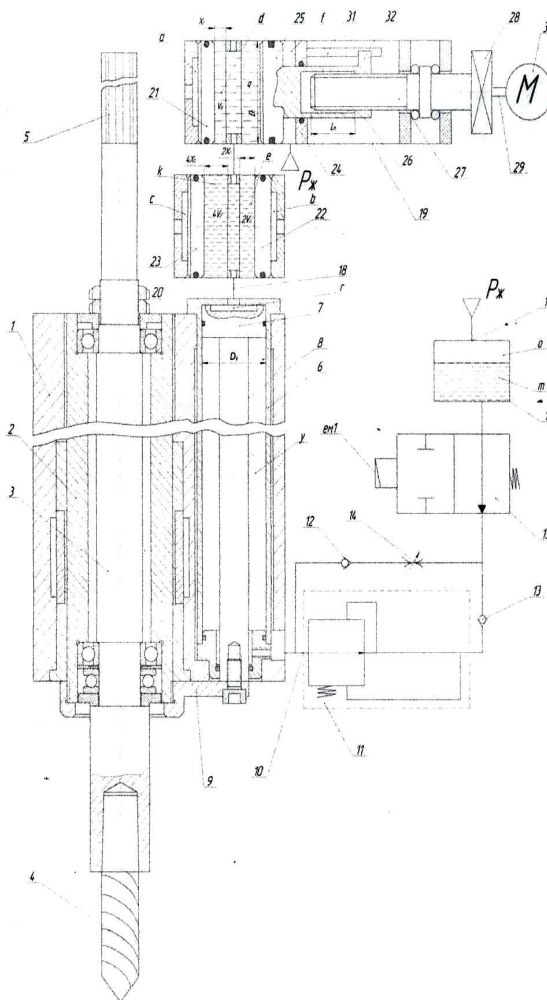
Привод осьової подачі шпинделя свердлильного верстата
